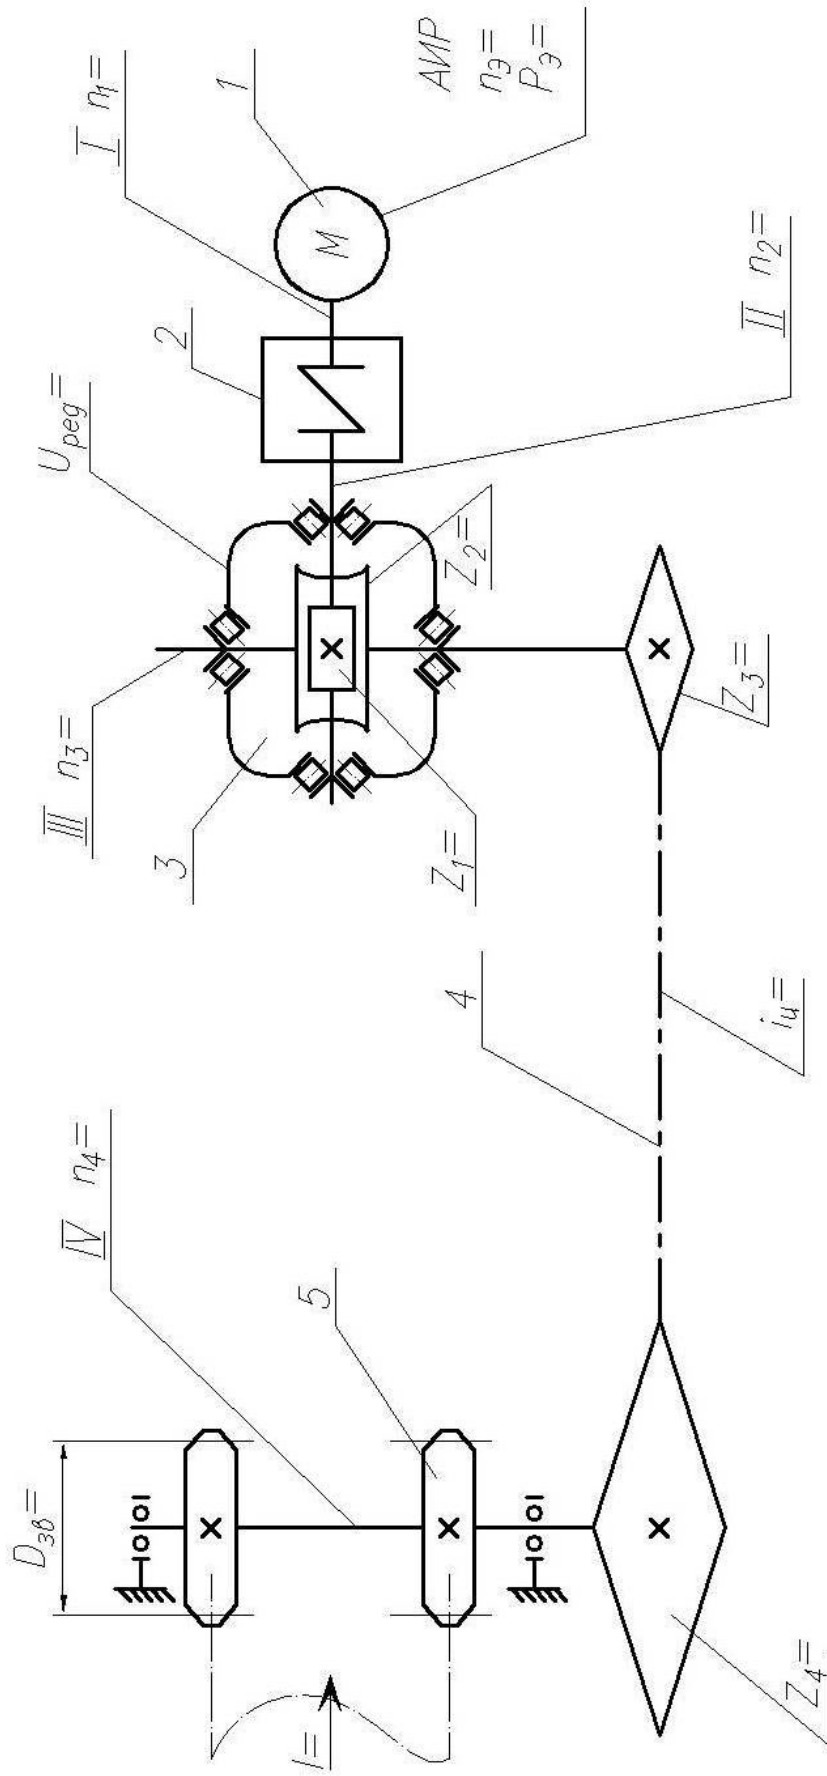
Кинематическая схема привода цепного конвейера (Привод 2):
